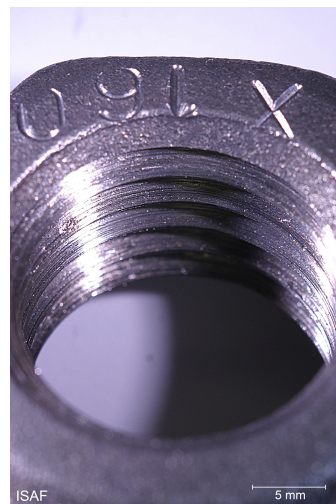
Gewindeprüfkörper axial belastet mit 160kN (Mutter)
